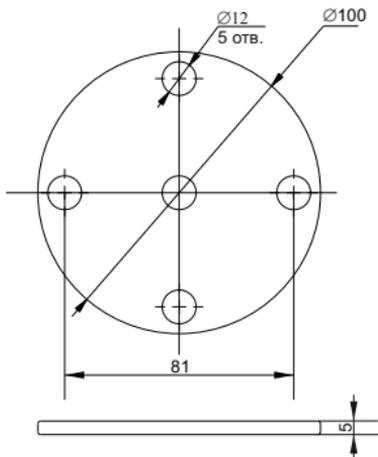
Габаритные размеры кольца / Figure 1 – Overall dimensions of the ring /
